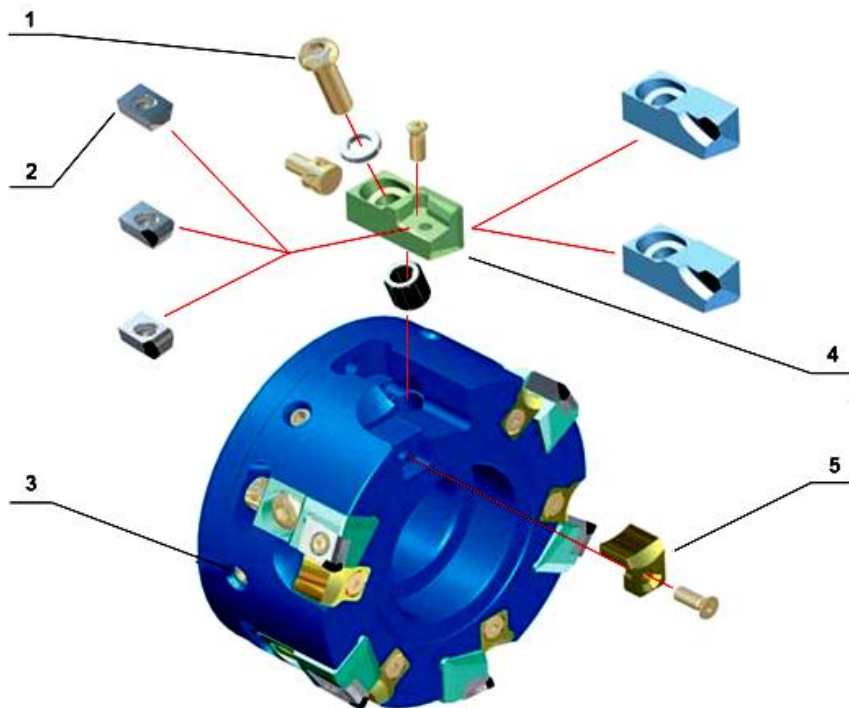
Крепление картриджей к корпусу фрезы фирмы «Sandvik Coromant»: 1 – винт крепежный; 2 – пластина режущая; 3 – винт балансирующий; 4 – картридж; 5 – пластина стружконаправляющая
